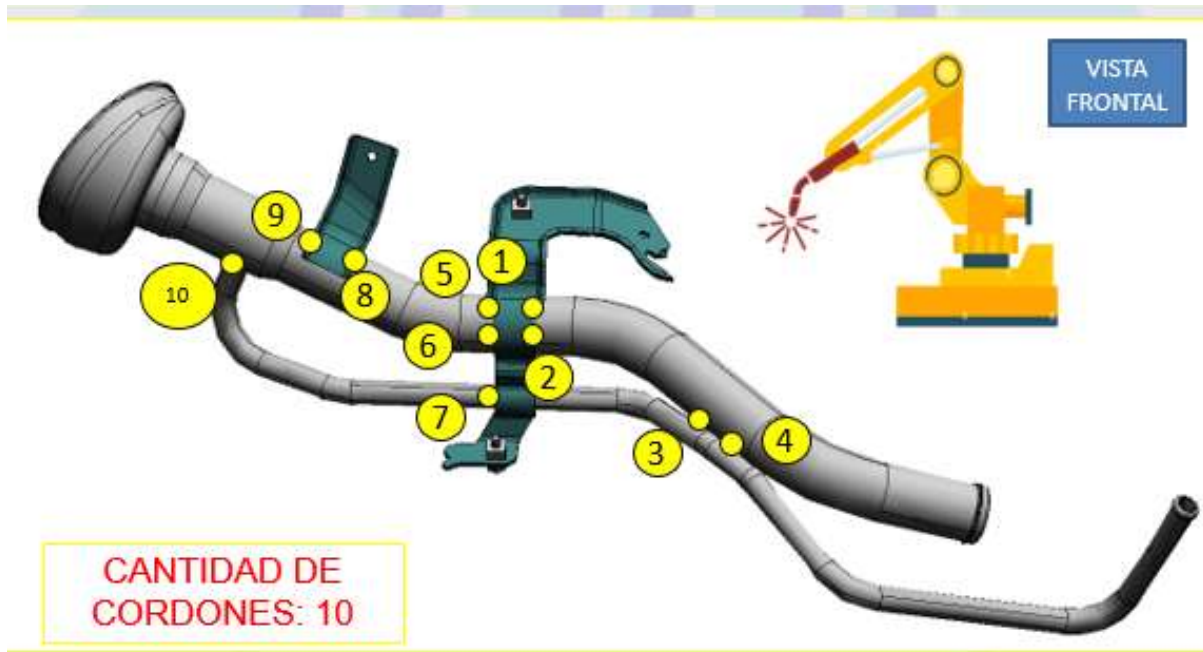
Dibujo de pieza con puntos de soldadura modificados
